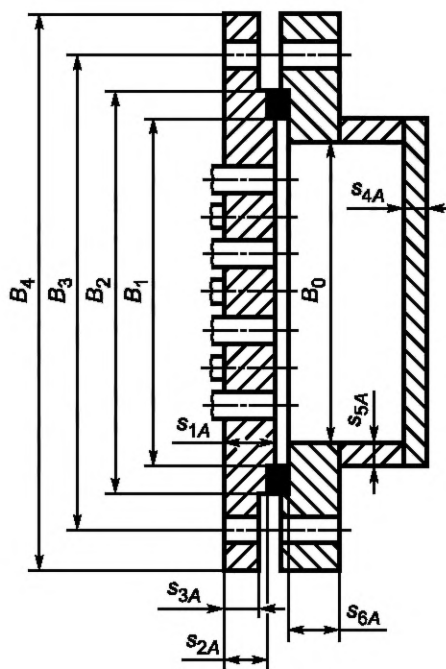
Камера разъемной конструкции со сварной крышкой
